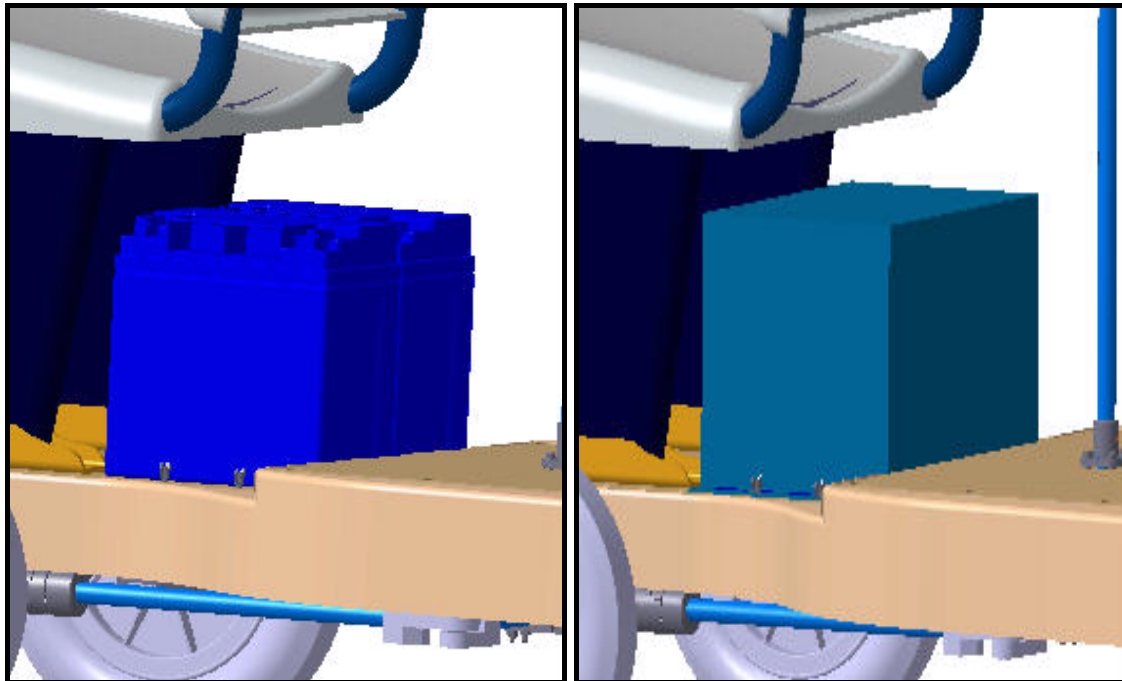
Detalle de las baterías y de la caja que las cubre.
